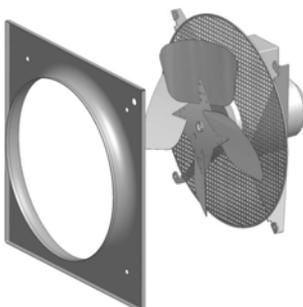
Ventilator in druckgekapselter Ausführung mit kurzer Einströmdüse
